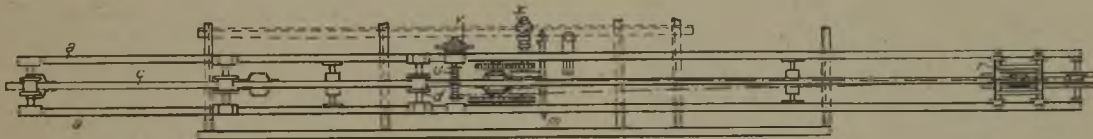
Grundriß der Planiervorrichtung von Heintzmann & Dreyer.
